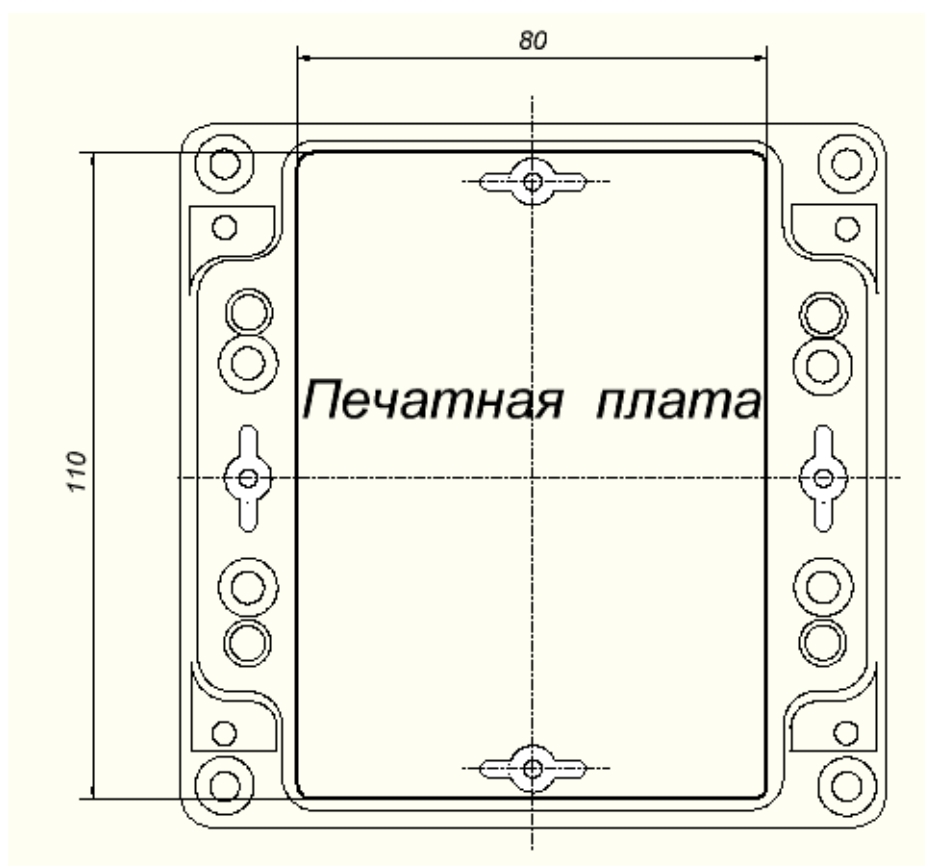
Схема компоновки печатной платы в корпусе G386/278 фирмы Gainta и габаритные размеры печатной платы
